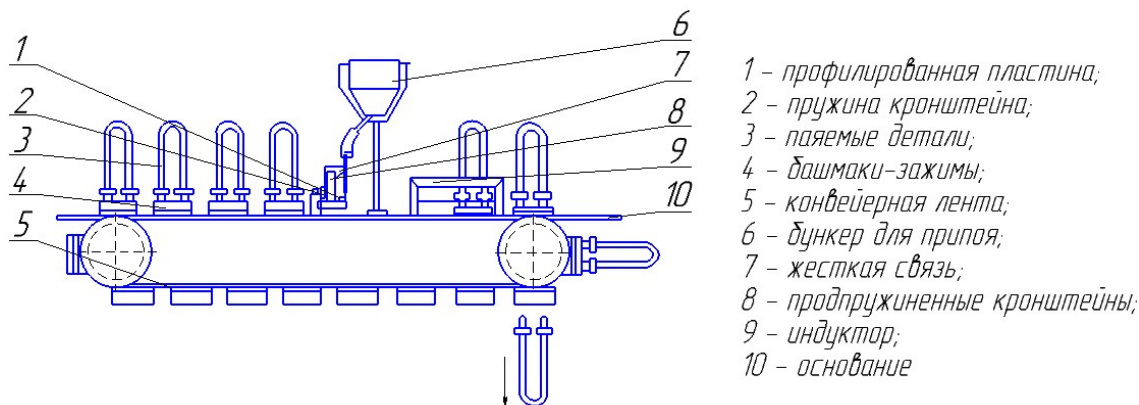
Общий вид установки для индукционной пайки трубчатых изделий
